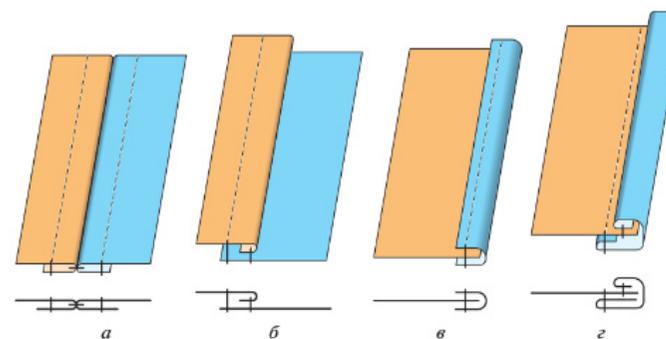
Виды швов: а — расстрочной; б — настрочной; в — окантовочный тесьмой; г — окантовочный с закрытым срезом
